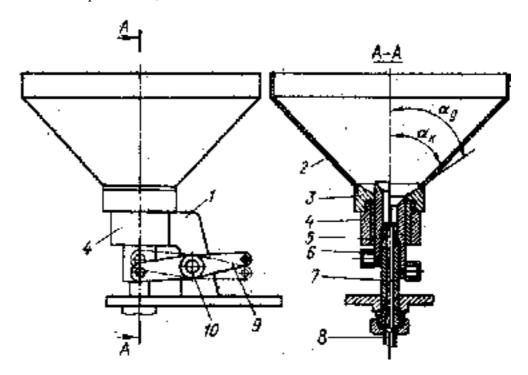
Конструкция бункера с захватно-орентирующими двумя подвтулками
